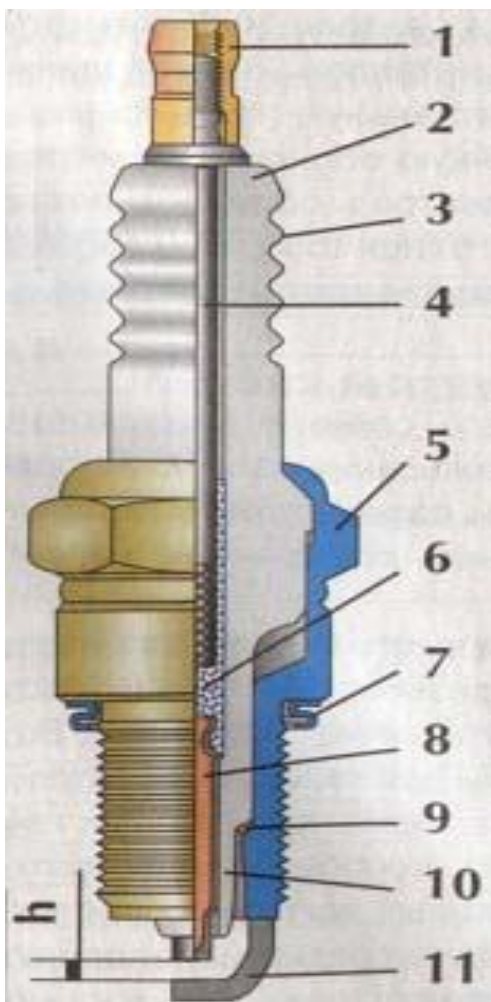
Устройство свечи зажигания с плоской опорной поверхностью: 1 - контактная (штекерная) гайка; 2 - изолятор; 3 - оребрение изолятора (барьеры тока); 4 - контактный стержень; 5 - корпус свечи; 6 - токопроводящий стеклогерметик; 7 - уплотнительное кольцо; 8 - центральный электрод с медным сердечником (биметаллический); 9 - теплоотводящая шайба; 10 - тепловой конус изолятора; 11 - боковой электрод ("массы"); h - искровой зазор.
